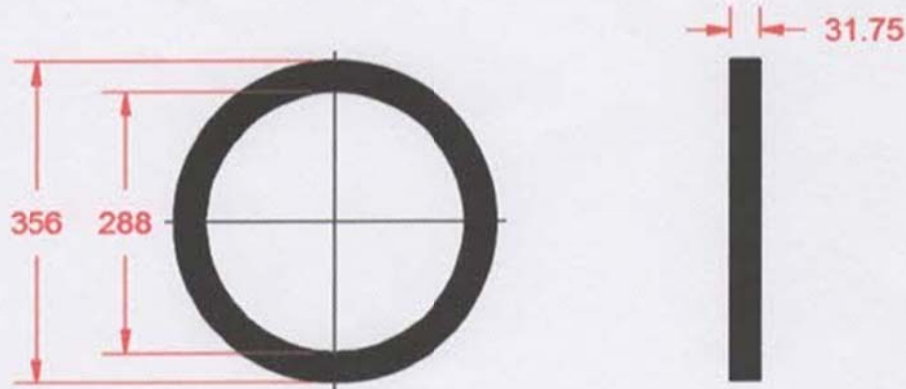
Dimensiones del neumático ISO 36 288 (mm)
